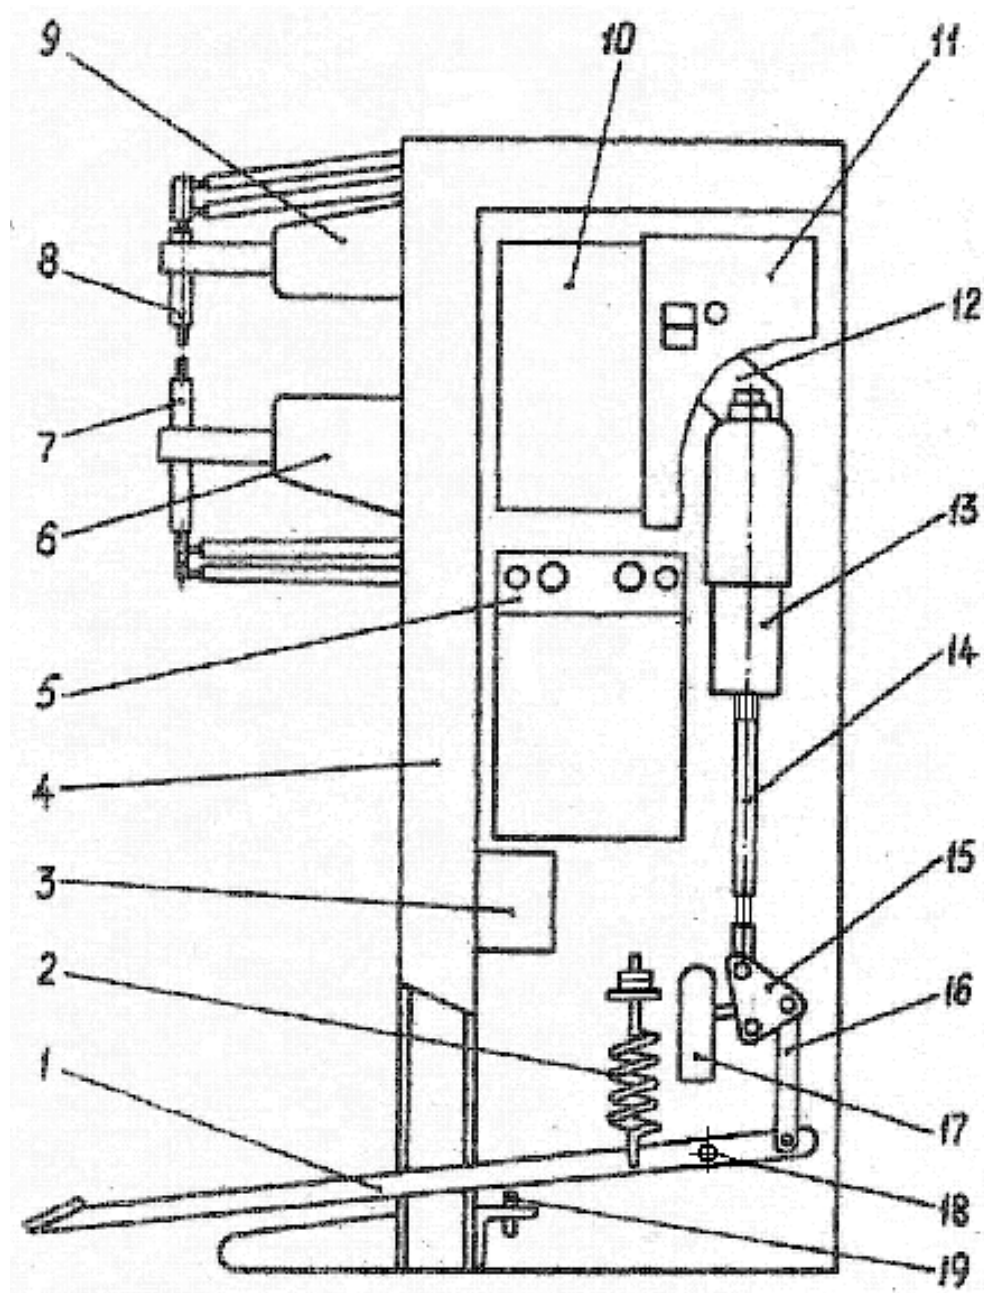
Схема устройства точечной сварочной машины МТ-601
